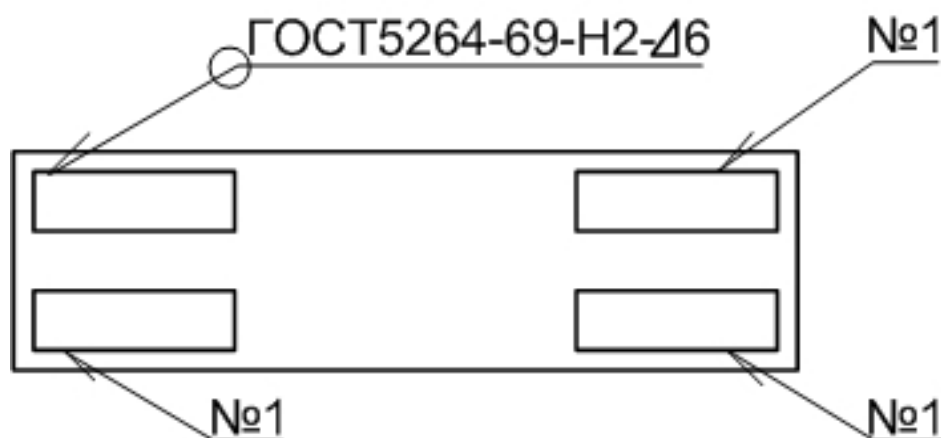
Обозначения сварных швов по ГОСТ 2.312-72
